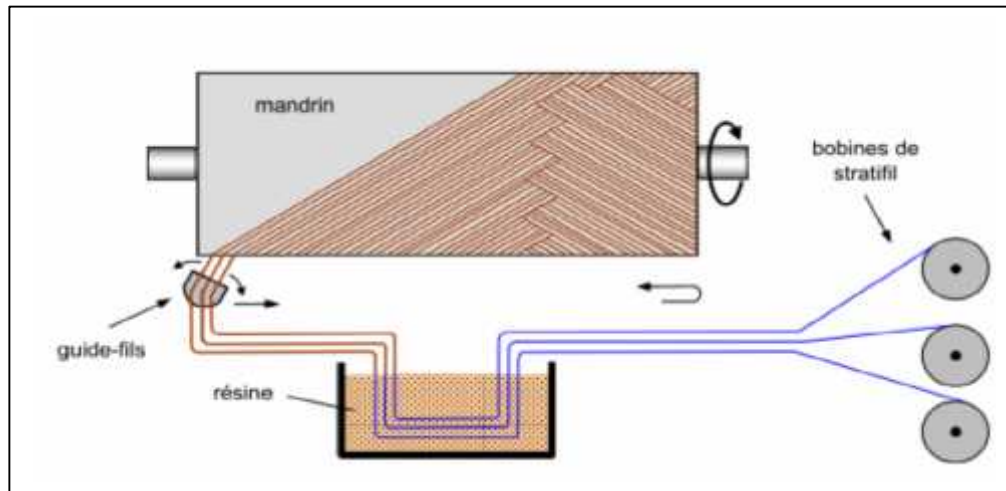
Principe d'enroulement hélicoïdal. [6]
